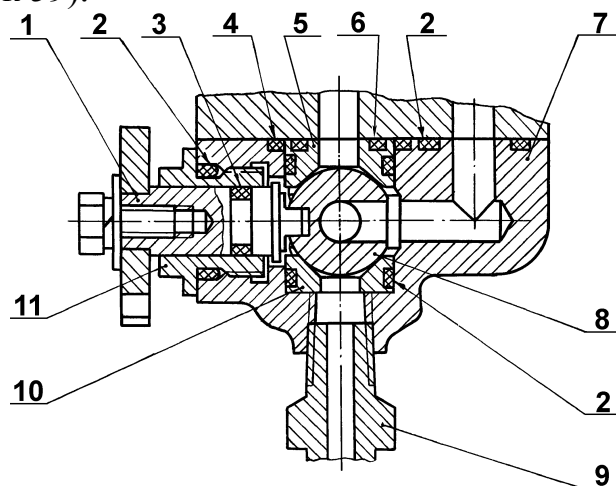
Кран сливной: 1 - ось; 5 - опора; 7 - корпус; 8 - шарик; 9 - штуцер; 10 - опора; 11 - втулка; 2,3,4,6 - кольца уплотнительные.
